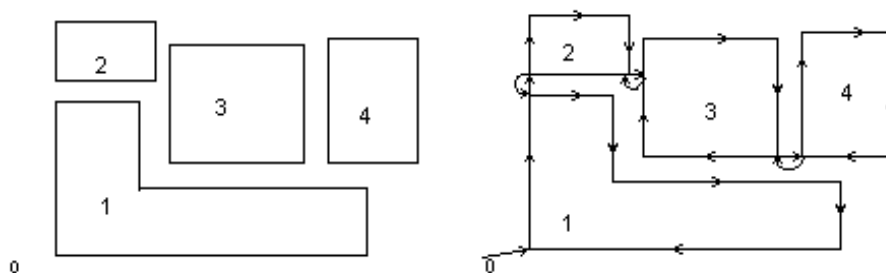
Conjunto de moldes e trajetória de corte usando “pontes”
